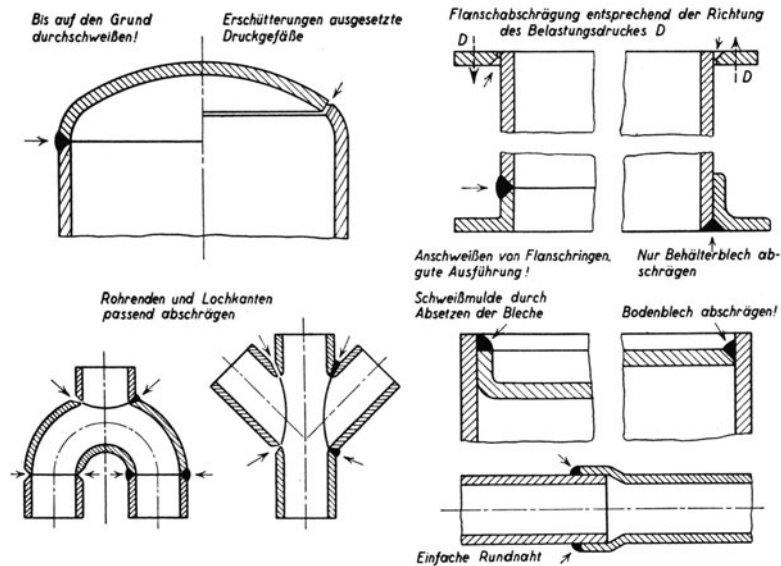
Rohrverbindungen durch Schweißen.
